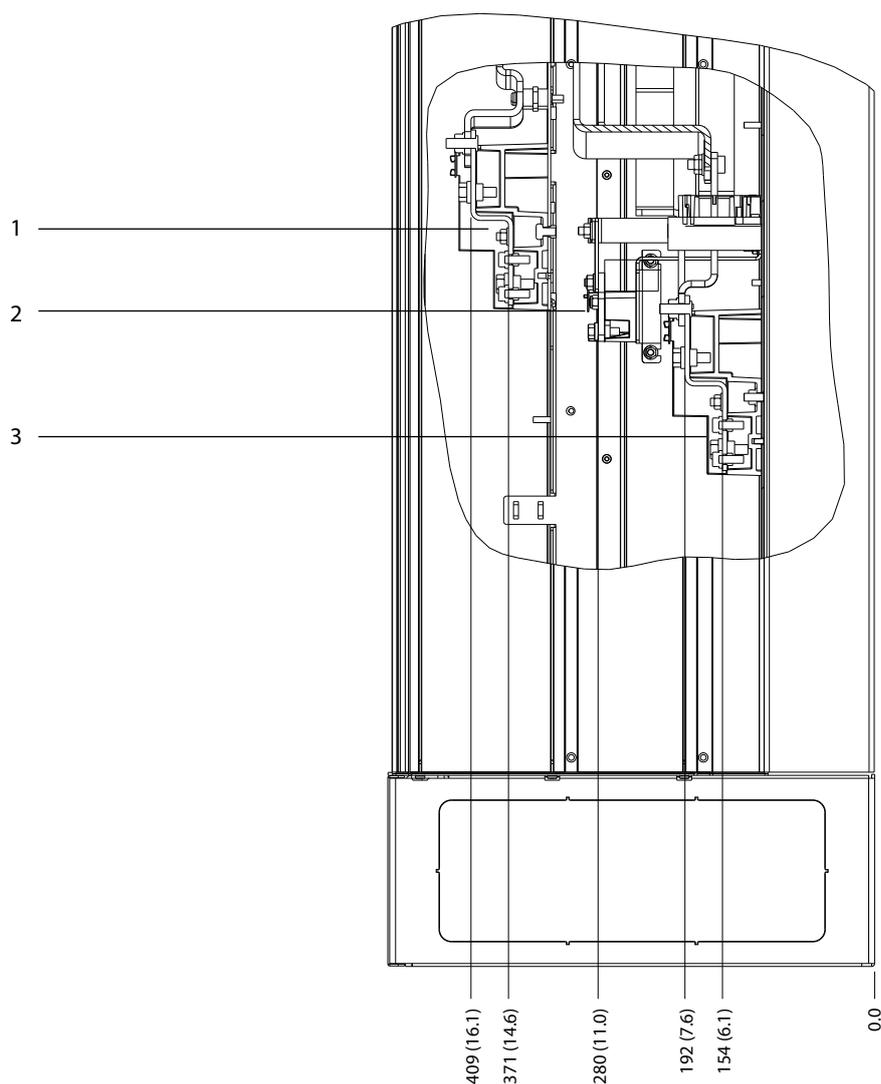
Dimensões detalhadas do terminal para E1/E2
